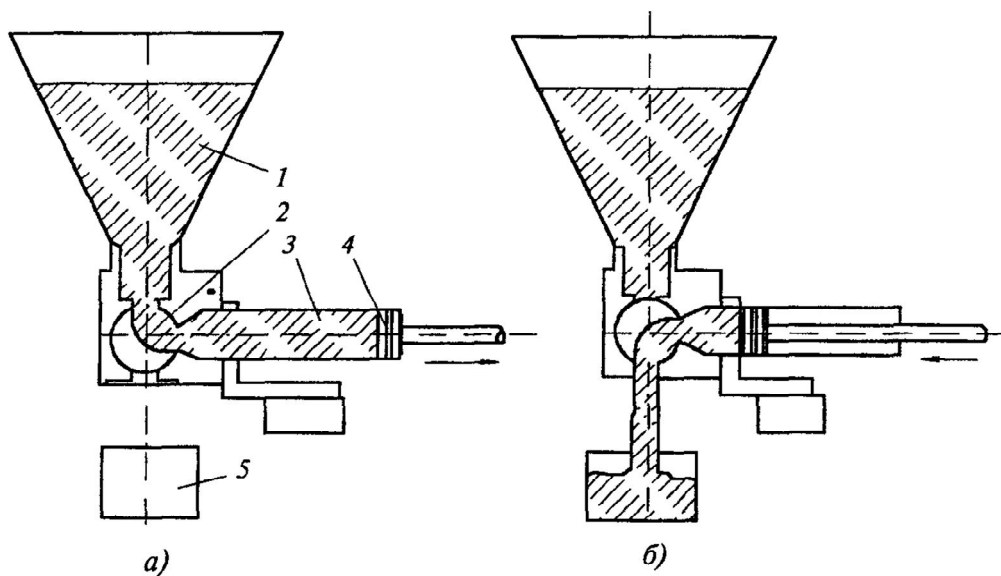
Принципова схема об'ємного поршневого дозатора:
